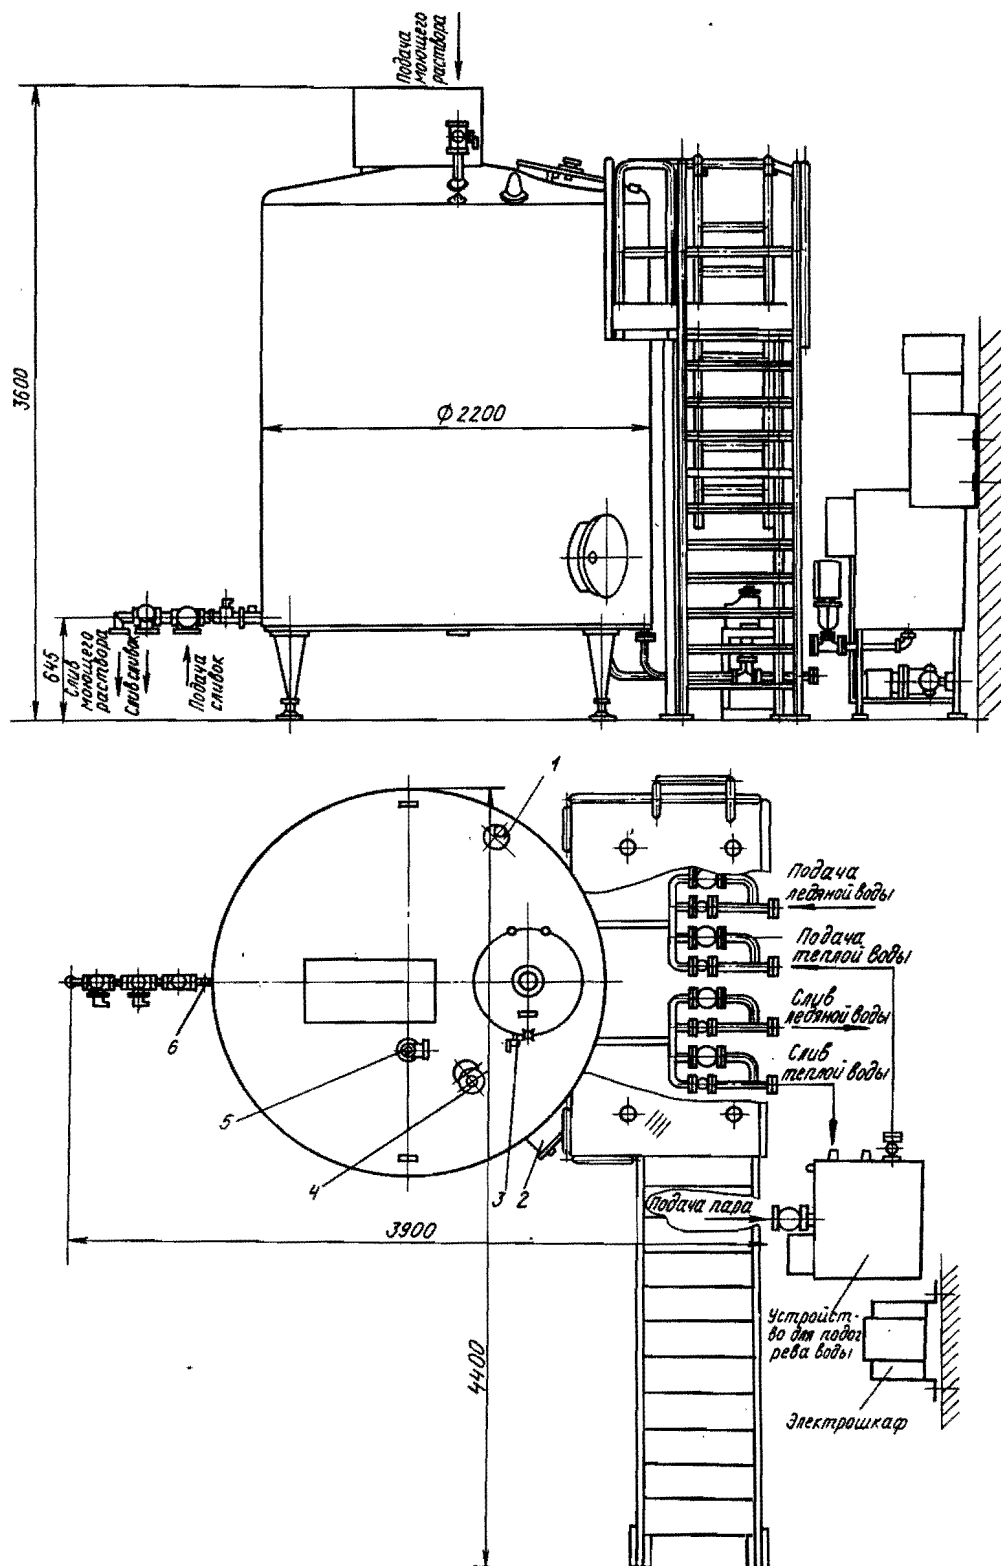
Общий вид резервуара сливкосозревательного марки Л5-ОТН-6300:
